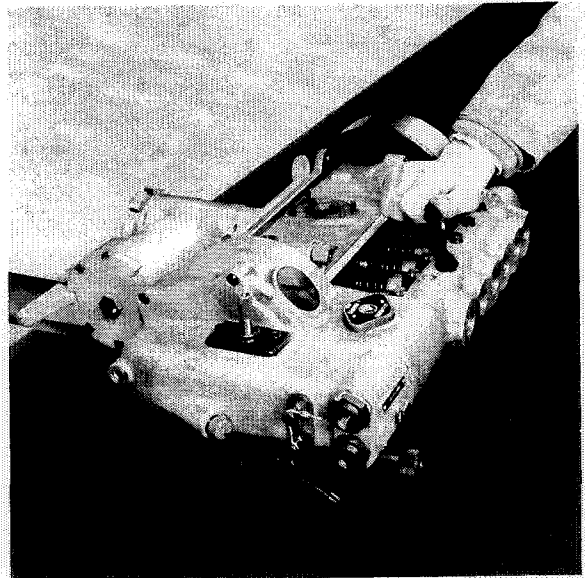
Lösen der Befestigungsschrauben für die Pumpenelemente
